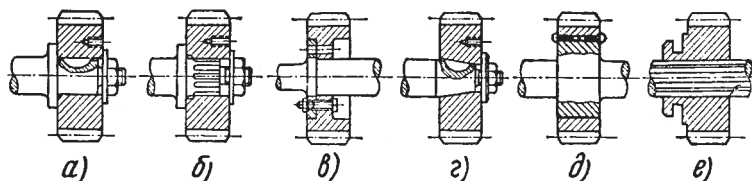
Способы закрепления зубчатых колес на валах:
